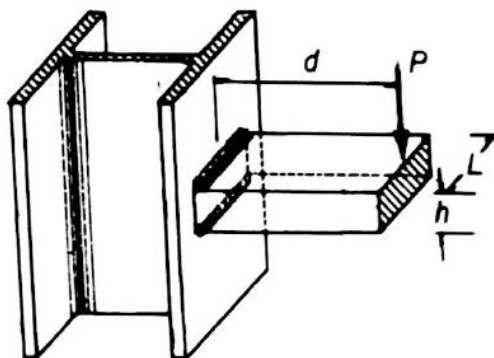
Unión soldada resistiendo a flexión con cordones frontales transversales.
